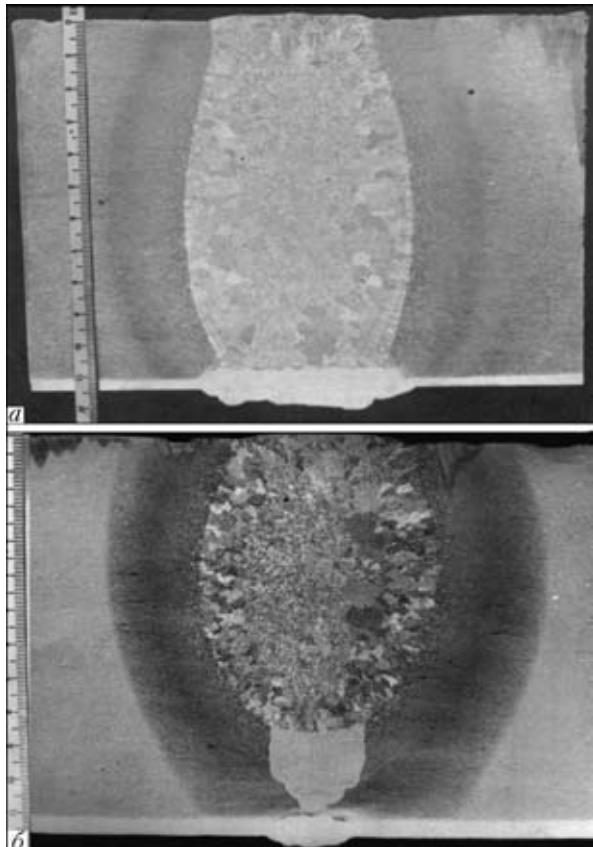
Макроструктура продольного шва штампосварного сосуда из биметалла 09Г2С + 0Х18Н10Т ($\delta = 170$ мм) с полным удалением плакирующего слоя в зоне сварки (а) и с комбинированной разделкой кромок, предусматривающей предварительную подварку основного слоя (б). Масса аппарата в рабочем состоянии 138 т
